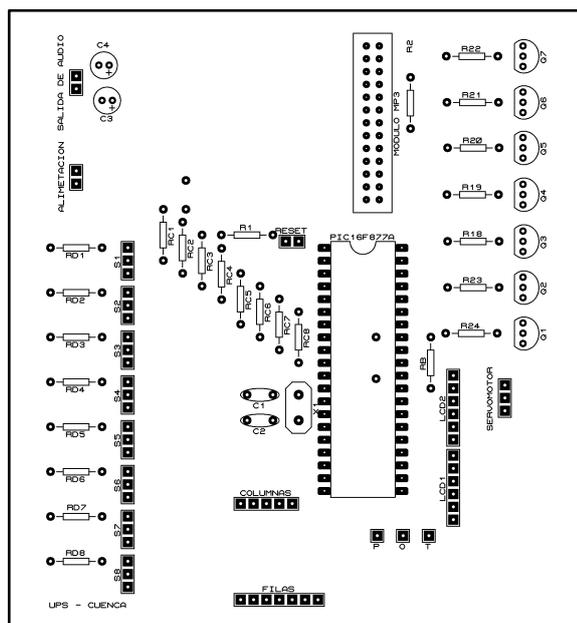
Disposición de componentes en PCB de Circuito Principal
